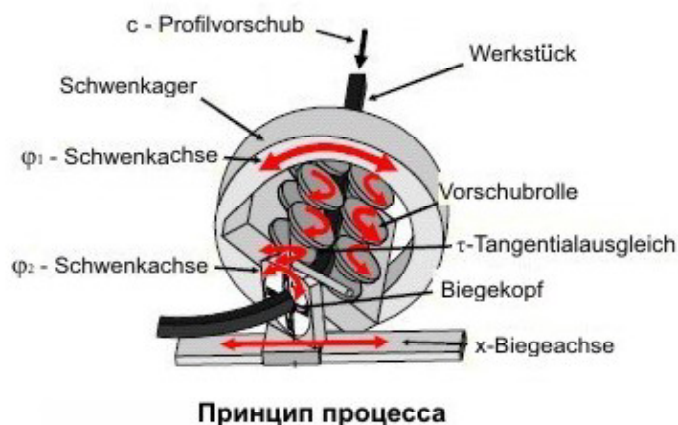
Машина для трехмерной гибки профилей: Vorschubrolle – роликовая система подачи; Biegekopf – изгибающая головка; Biegeachse – ось изгиба; Schwenkachse – поворотная ось
